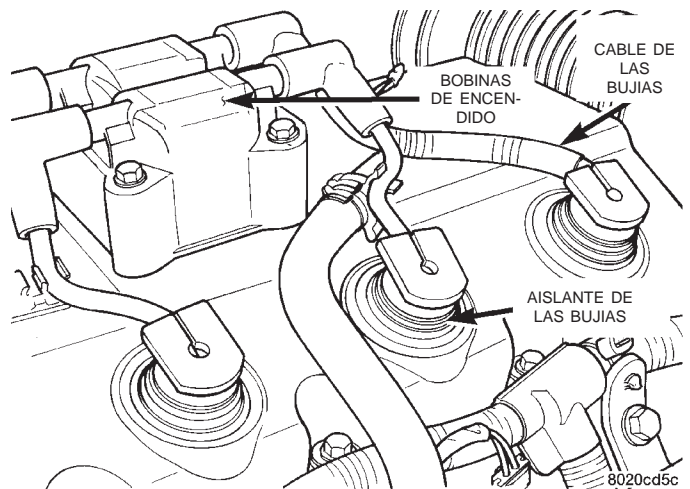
Conjunto de bobina de encendido — Motor 2.0L
